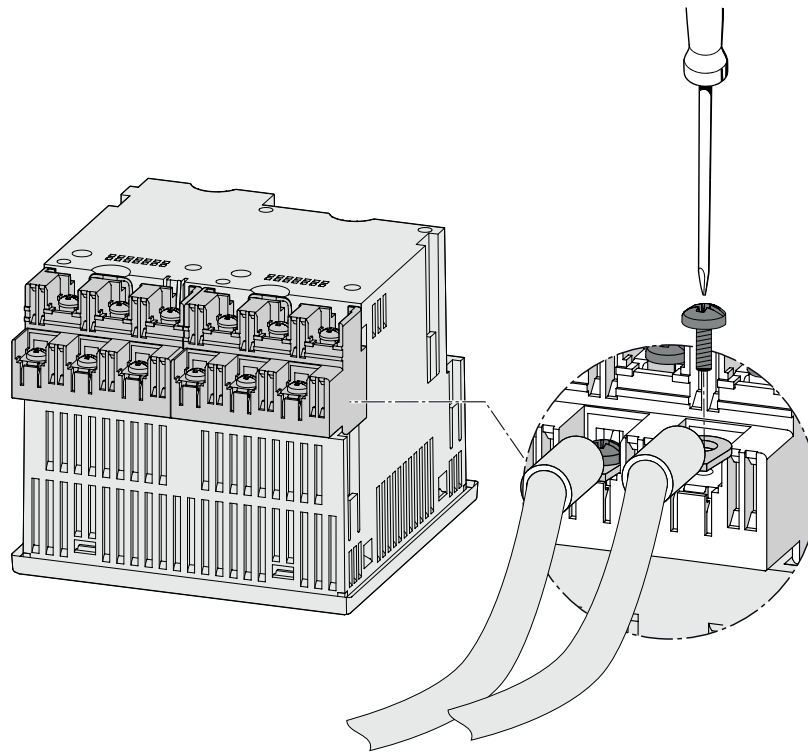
Conexión de los cables en las conexiones para terminales de ojal:
